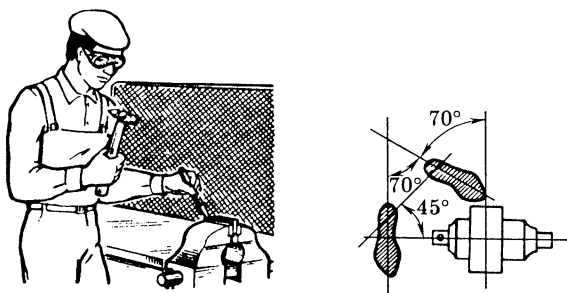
Положение корпуса и ног при рубке зубилом
